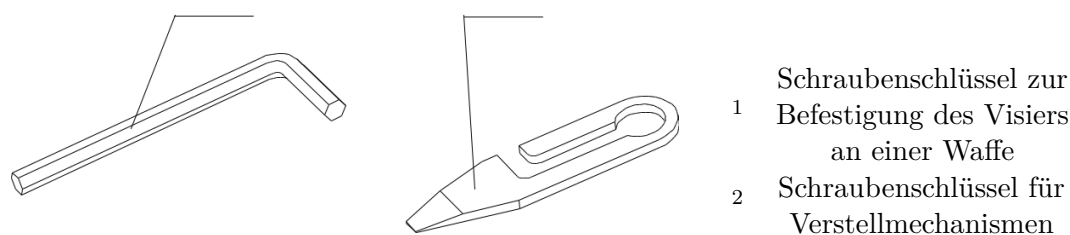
Gesamtansicht der Schraubenschlüssel
